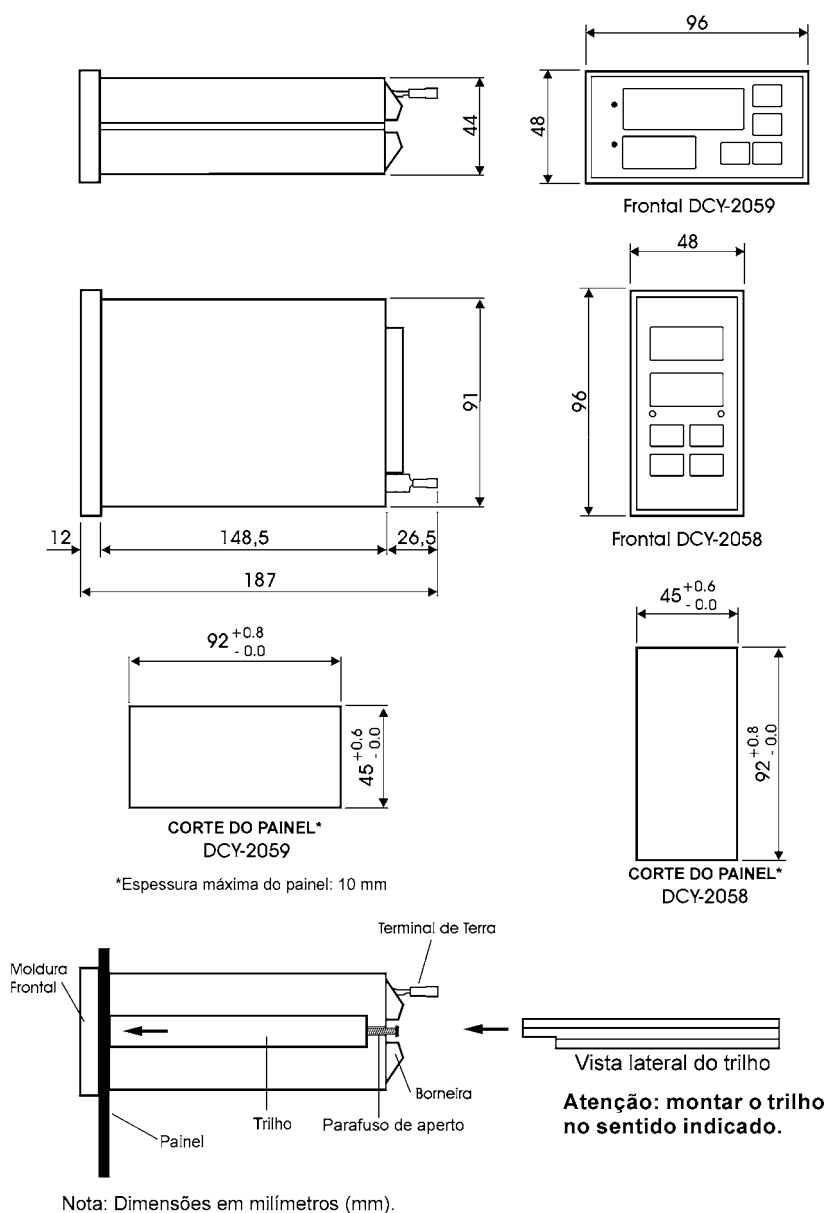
Desenho dimensional, corte e vista lateral da montagem no painel
